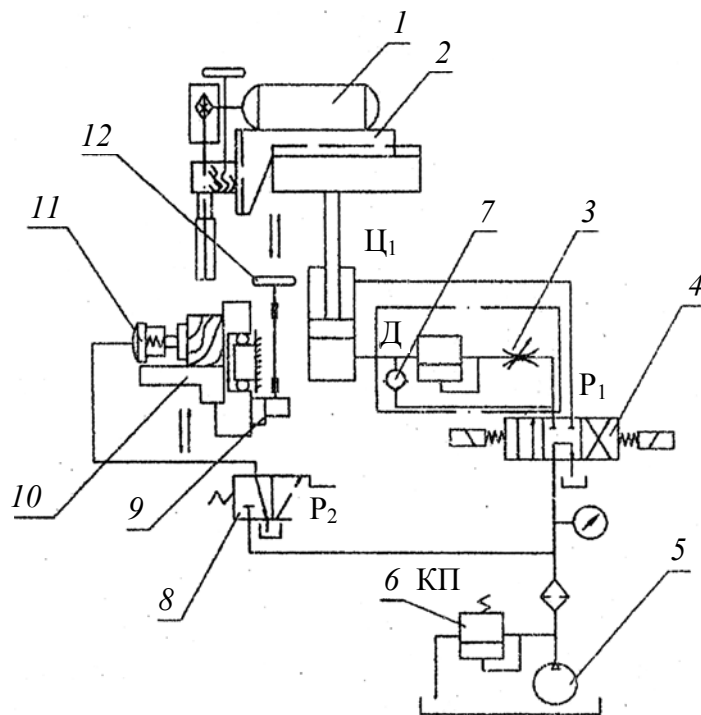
Гидравлическая схема цепнодолбежного станка ДЦА-3
